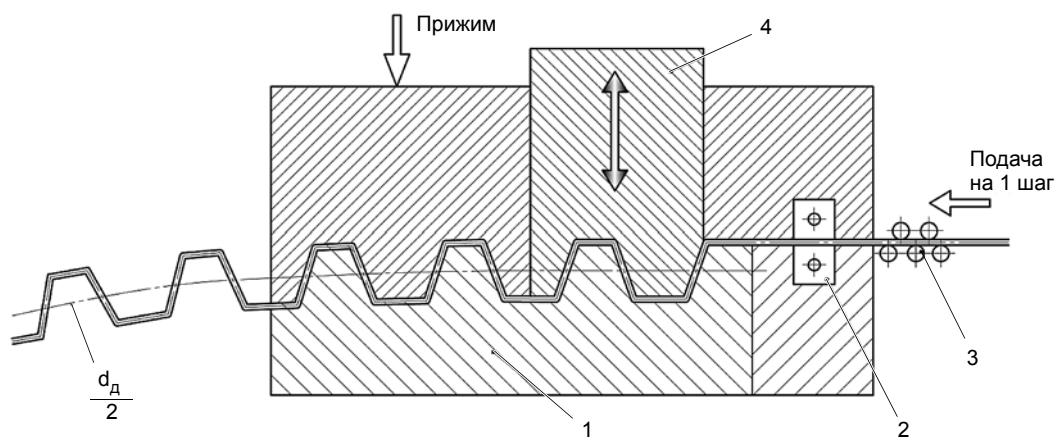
Схема формирования гнутого зубчатого профиля с использованием специального профилирующего пресса: 1 — матрица; 2 — нагревательный элемент; 3 — механизм подачи; 4 — пуансон; $t = \pi m$ — шаг зубьев по делительной окружности
